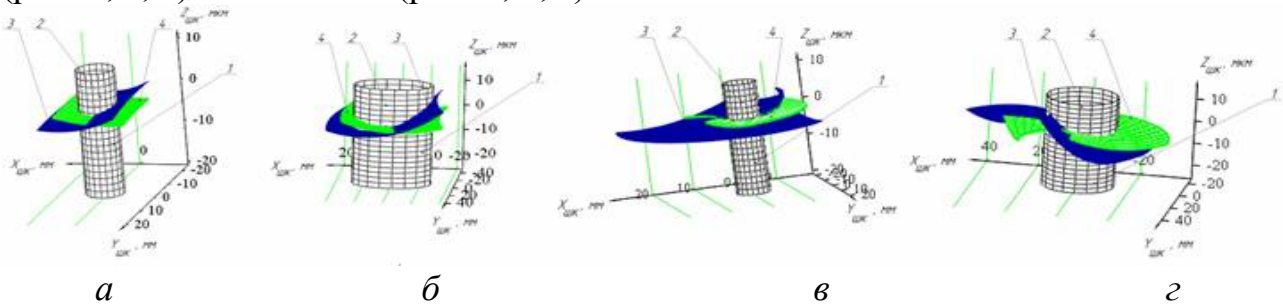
Точність формоутворення торця штовхача при обробці шліфувальним кругом з калібруючою ділянкою деталей що не обертаються під час обробки а, б та обертаються під час обробки в, г
